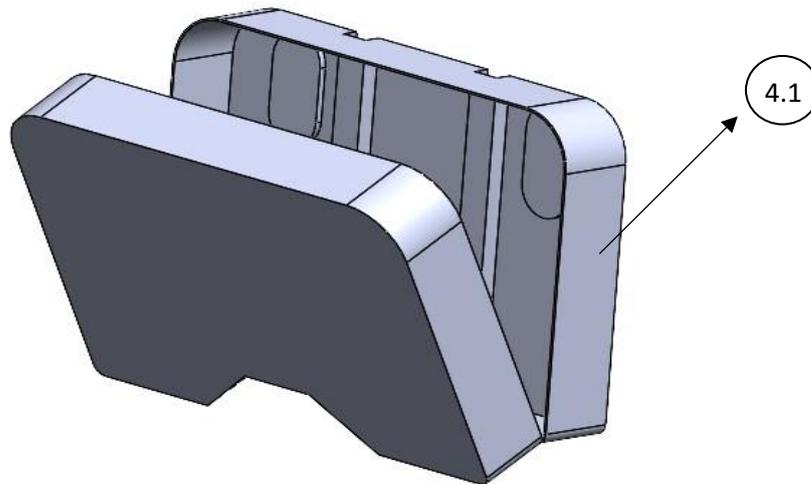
Ensamblaje subconjunto 2 (2)
